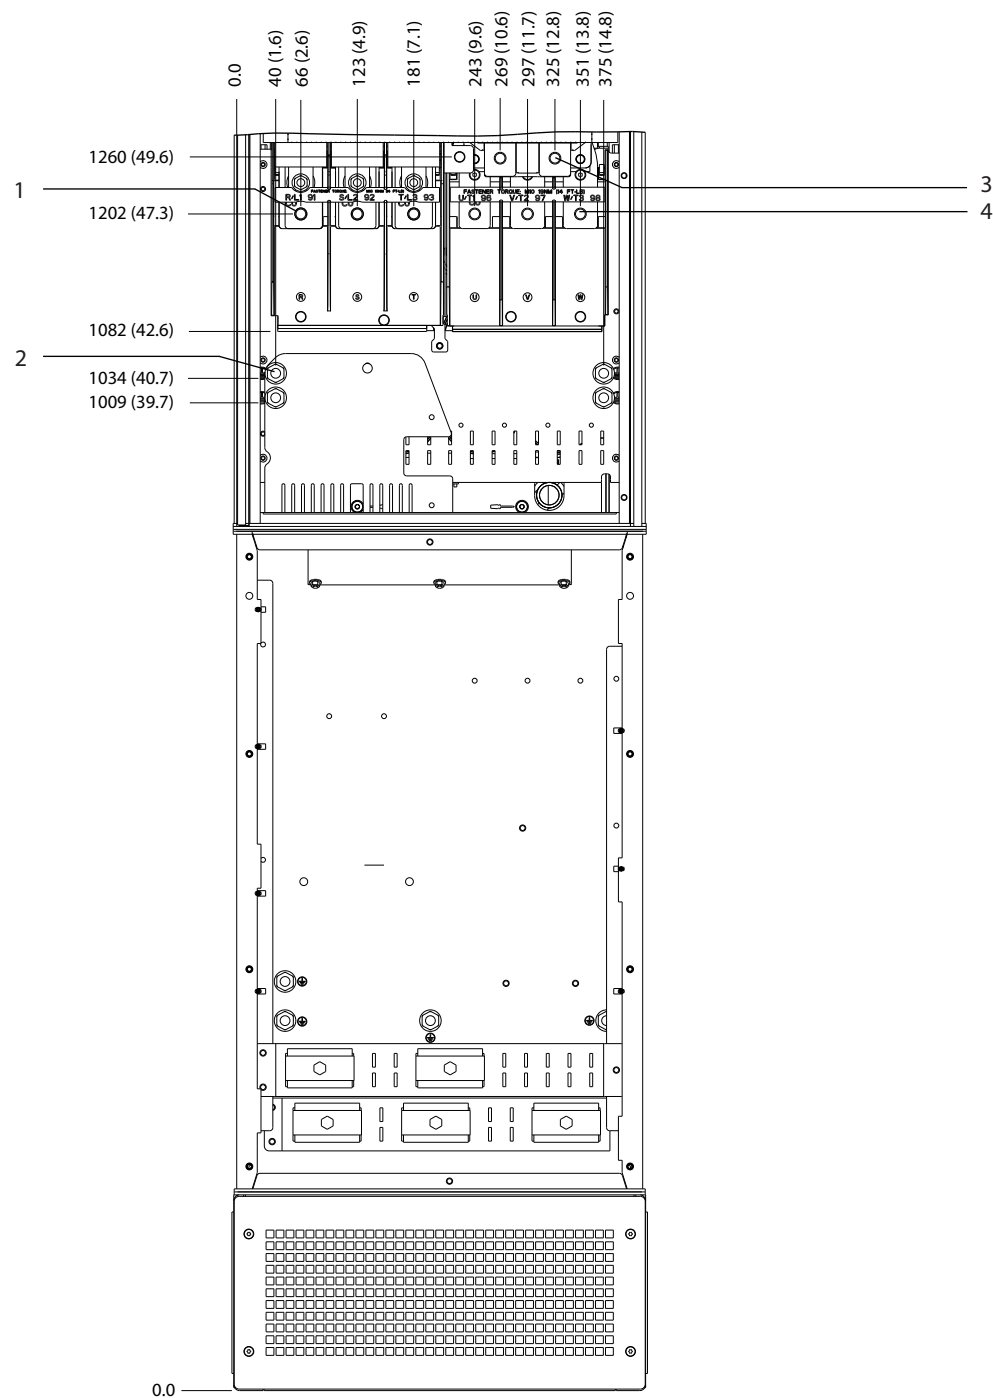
Dimensions des bornes D7h avec option sectionneur (vue frontale)
